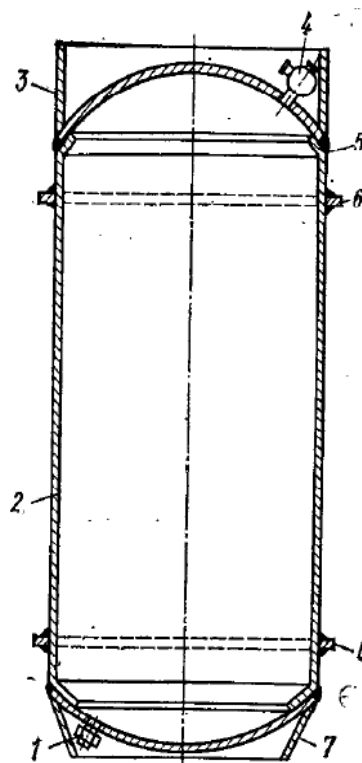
Контейнер для транспортирования и хранения UF_6 : 1 – пробка; 2 – корпус; 3 – верхняя юбка; 4 – клапан; 5 – сварной шов; 6 – ребра жесткости; 7 – нижняя юбка
